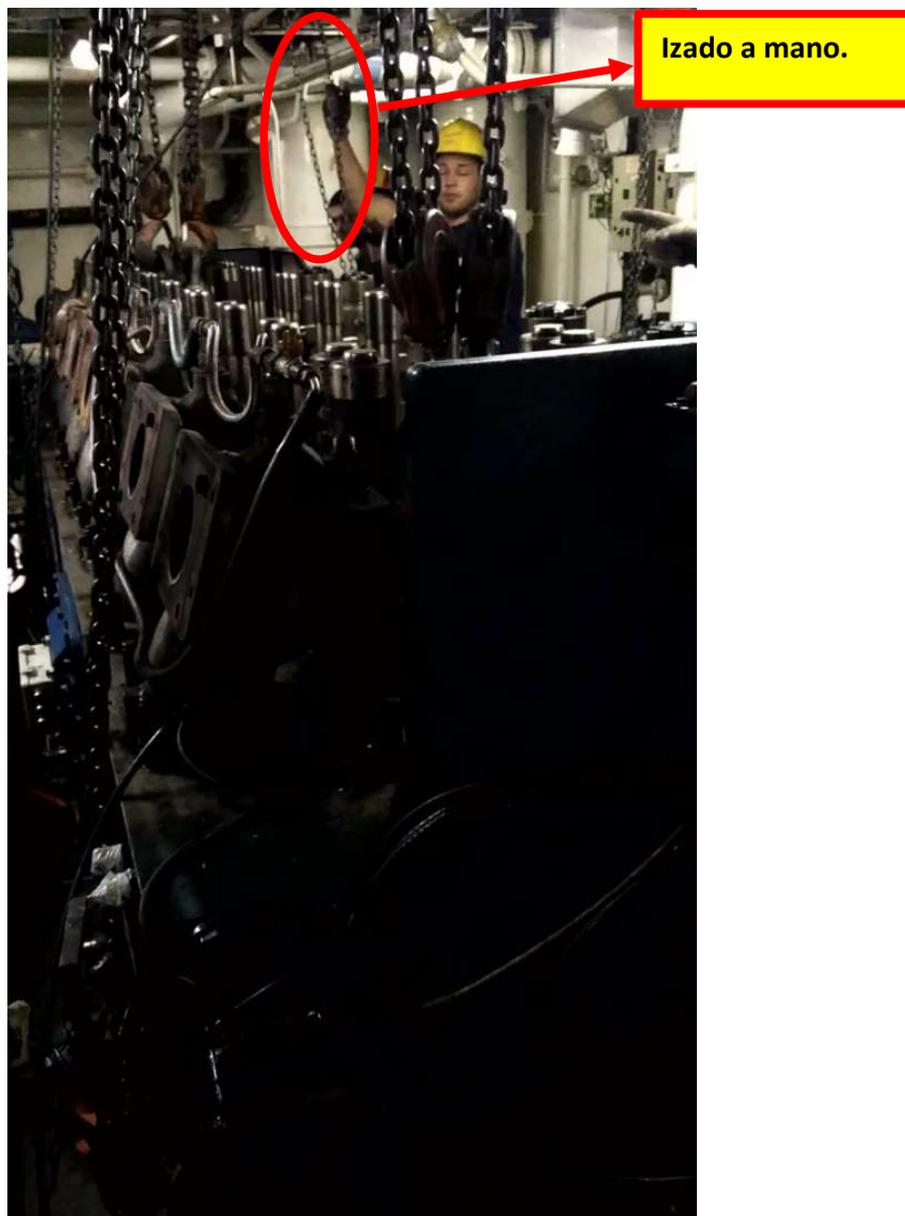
Izado del bloque. Fuente: Trabajo de campo.
